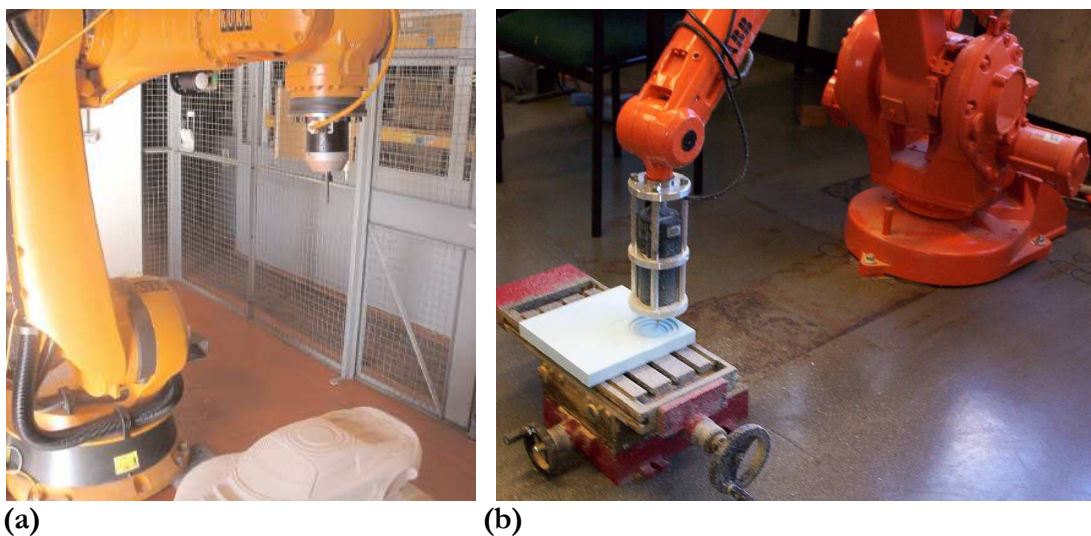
Usinage par robot industriel : robot Kuka (a) et robot ABB (b)
